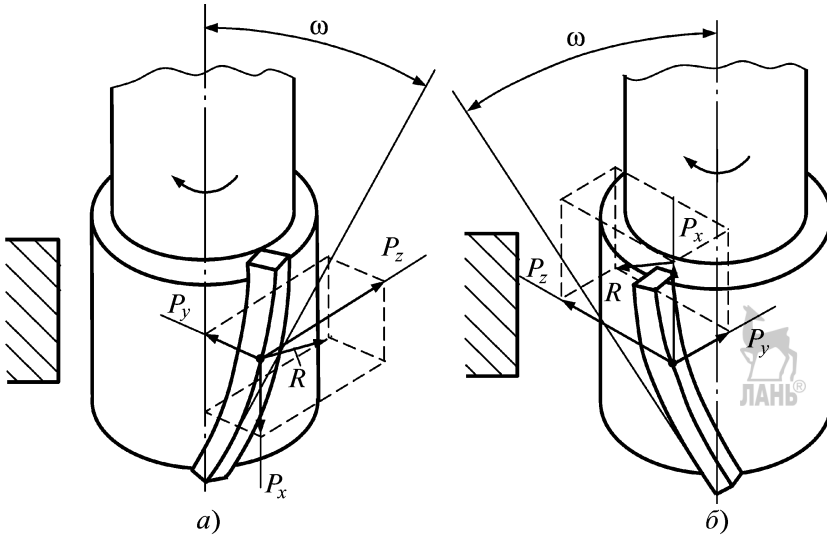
Схема сил, действующих на зуб фрезы при резании
